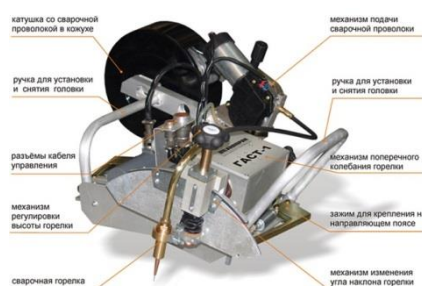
Универсальная сварочная головка ГАС-1
